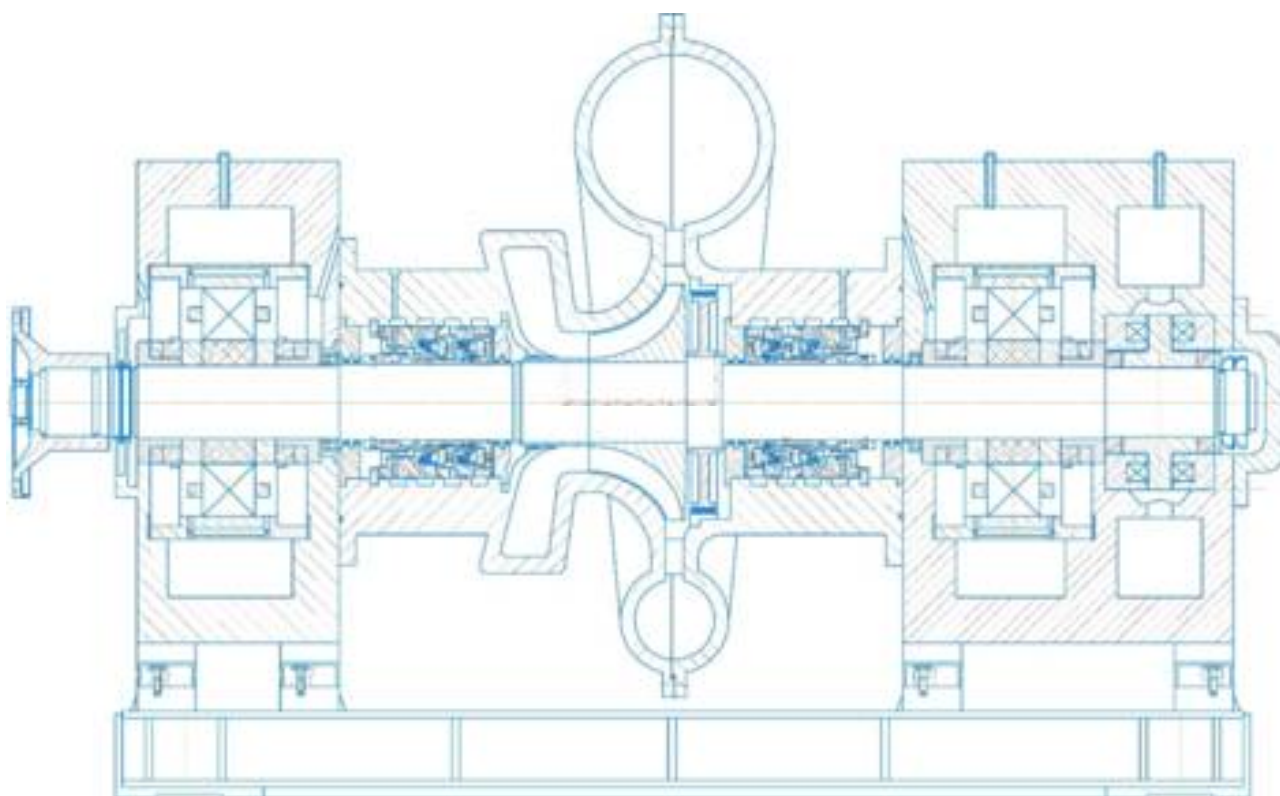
Одноступенчатый компрессор двухпорного исполнения
